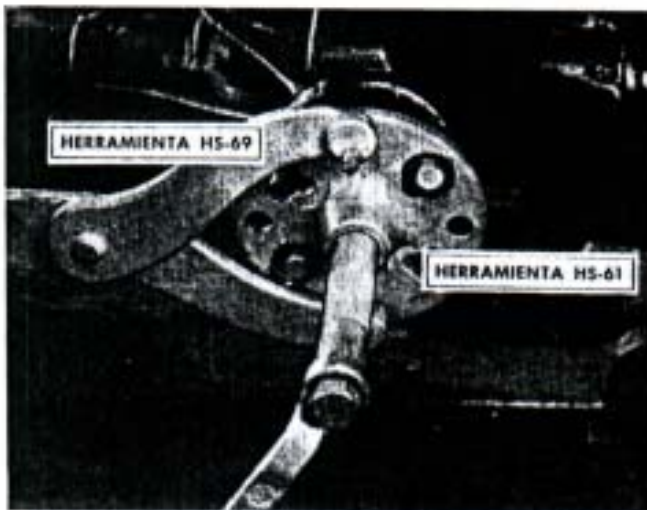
Extrayendo la horquilla de la junta universal con la herramienta HS-61 y HS-69.
